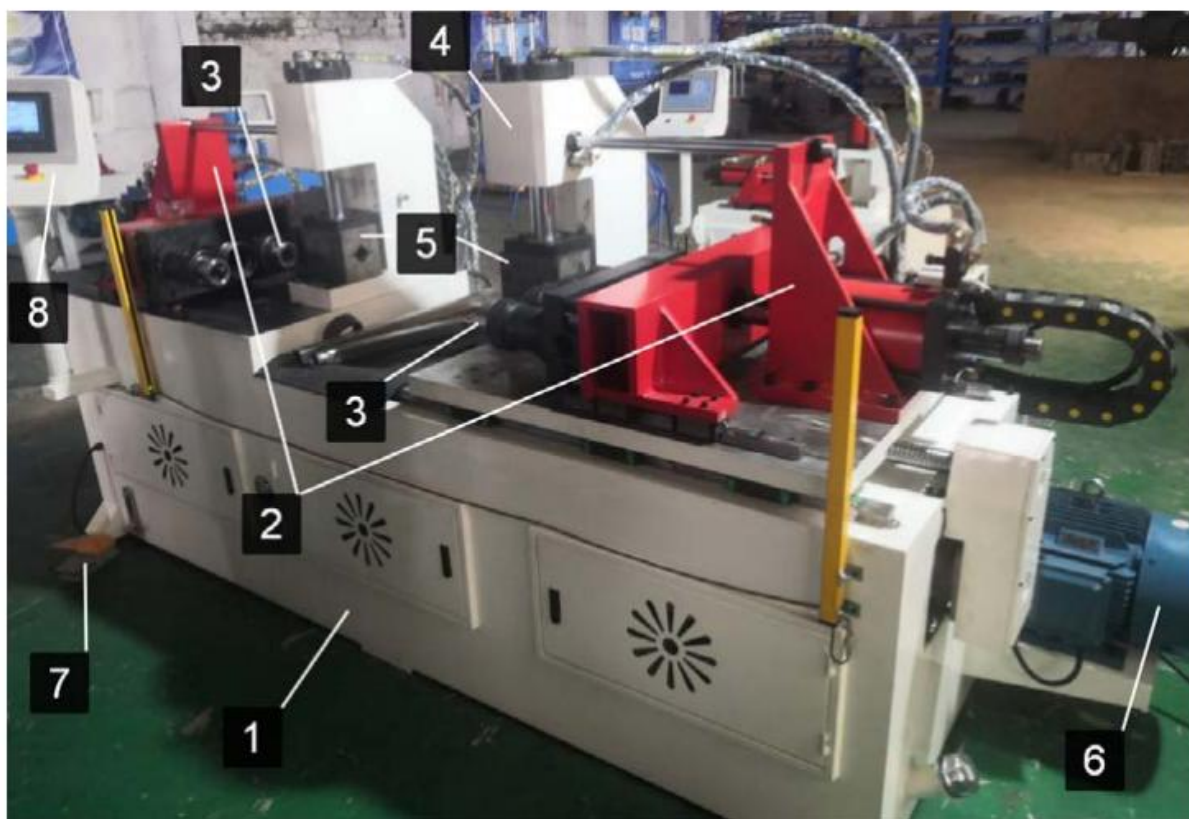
Гидравлическая установка для обжима трубной заготовки:
